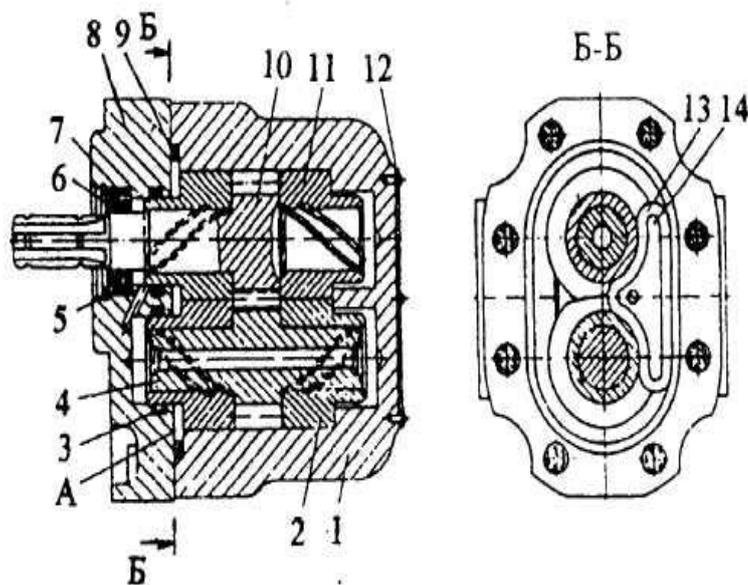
Сборочный чертёж шестеренного насоса типа НШ-32
